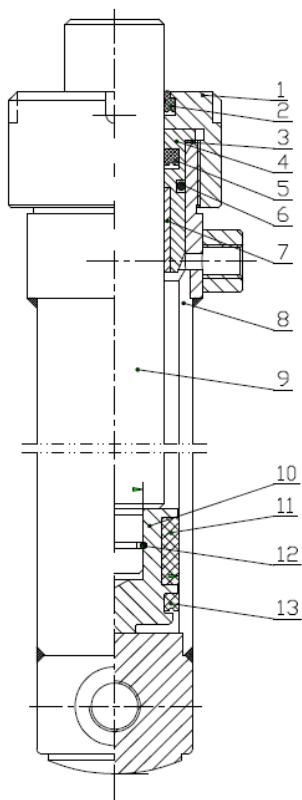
Цилиндр подъёма (левый цилиндр)
